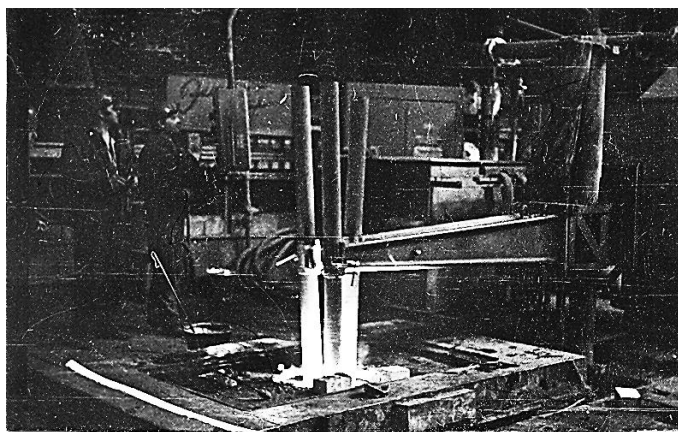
Электрошлаковый обжиг головной части заготовки диаметром 520 мм
